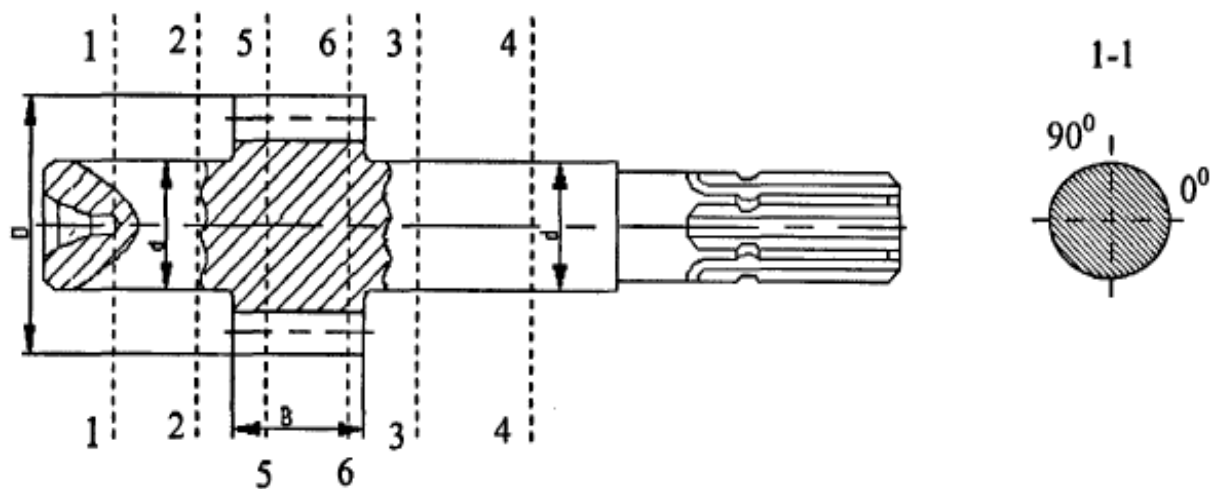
Схема вимірювання приводного валу шестерні
